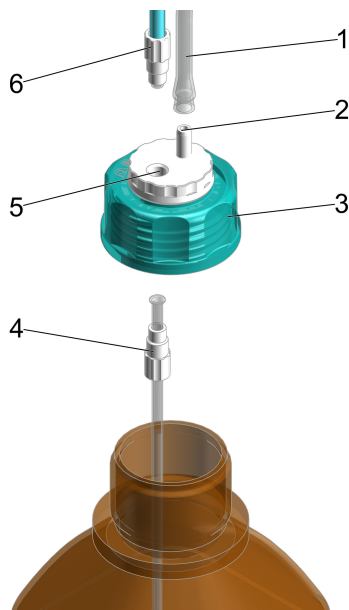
Bestücken des Siphon Breaker für die Reagenzflasche (Solvent)
